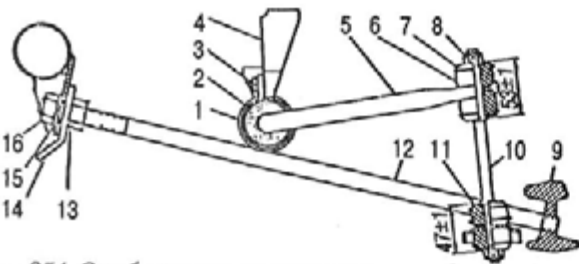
Стабилизатор и растяжка к передней подвеске: 1 - обойма; 2 - резиновая втулка; 3 - болт с гайкой; 4 - кронштейн; 5 - штанга; 6 - верхняя резиновая подушка; 7 - чашка; 8 и 16 - гайка; 9 - поперечина подвески; 10 - стойка; 11 - нижняя резиновая подушка; 12 - растяжка; 13 - контрогайка; 14 - транспортировочная скоба; 15 - шайба
